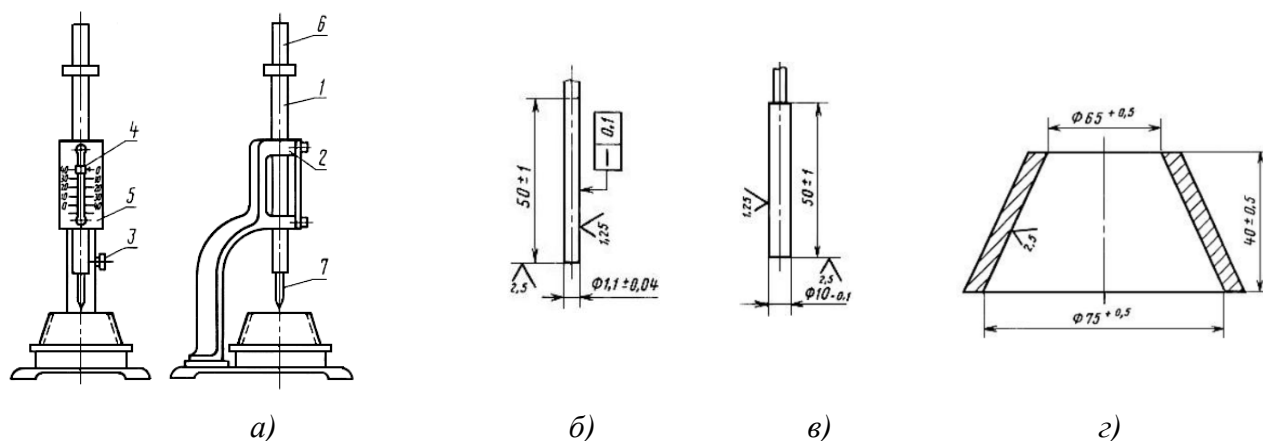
Прибор Вика: а – общий вид прибора; б – игла; в – пестик; г – кольцо
